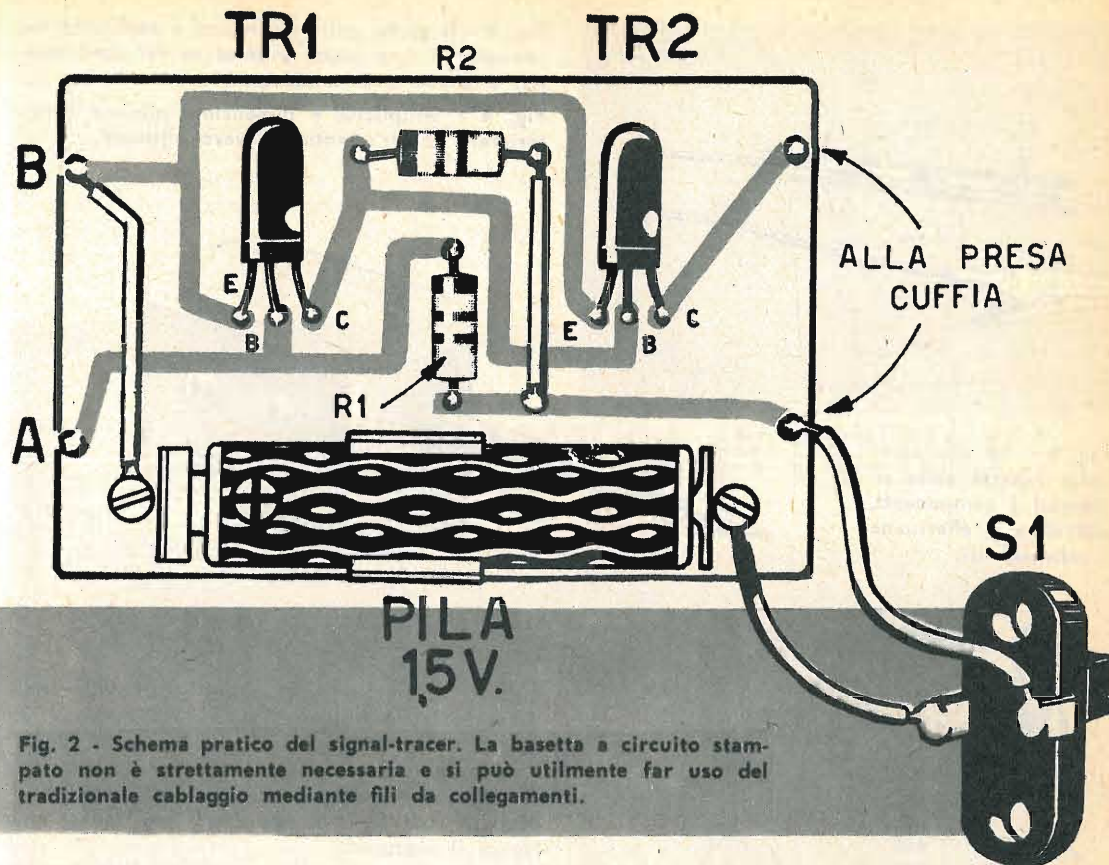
Schema pratico del signal-tracer. La bassetta a circuito stampato non è strettamente necessaria e si può utilmente far uso del tradizionale cablaggio mediante fili da collegamenti.
